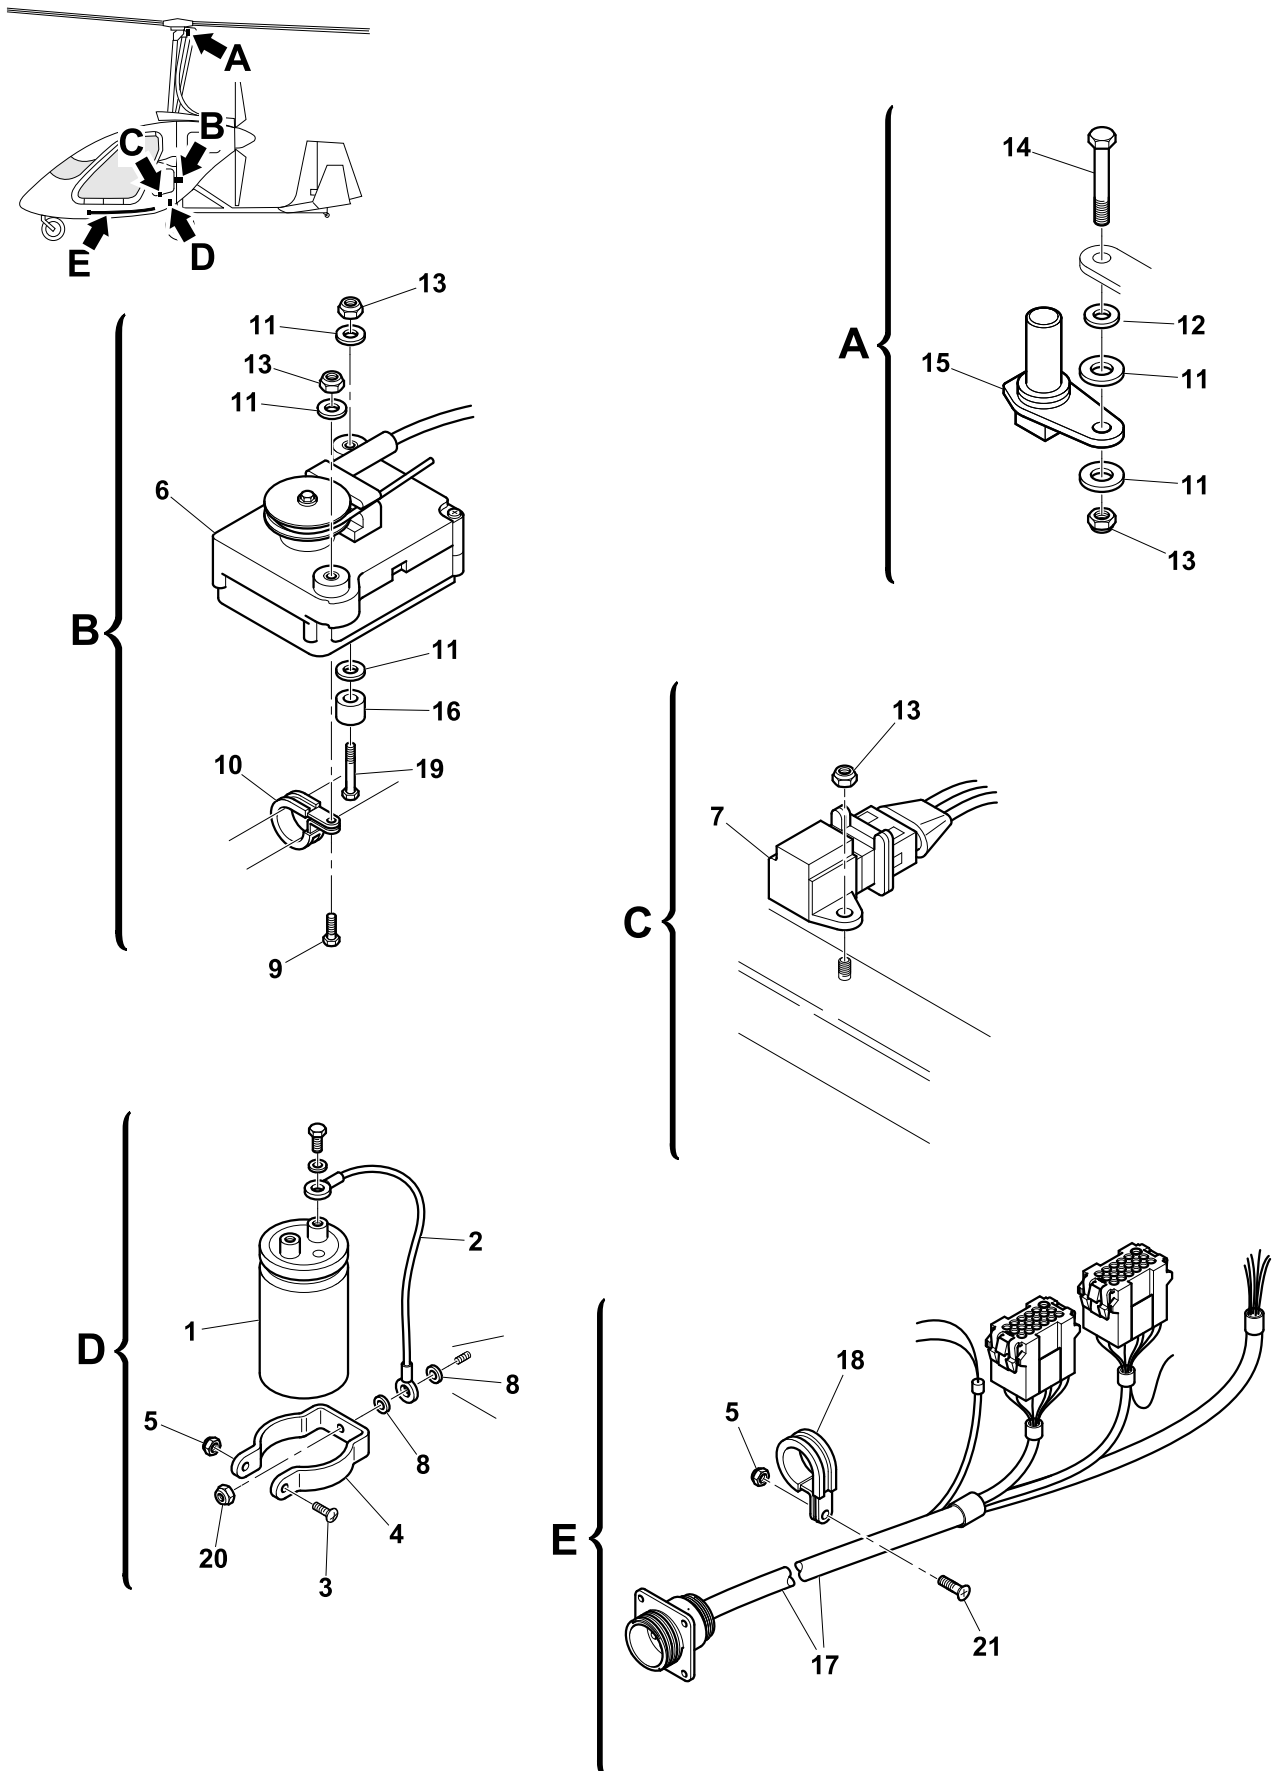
COMPONENTI ELETTRICI 2^a parte
